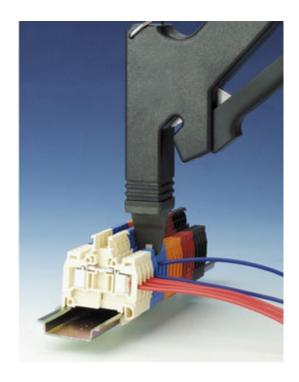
A.D.O.-Schneidklemmtechnik unter Verwendung eines Werkzeugs (Foto: ABB)
